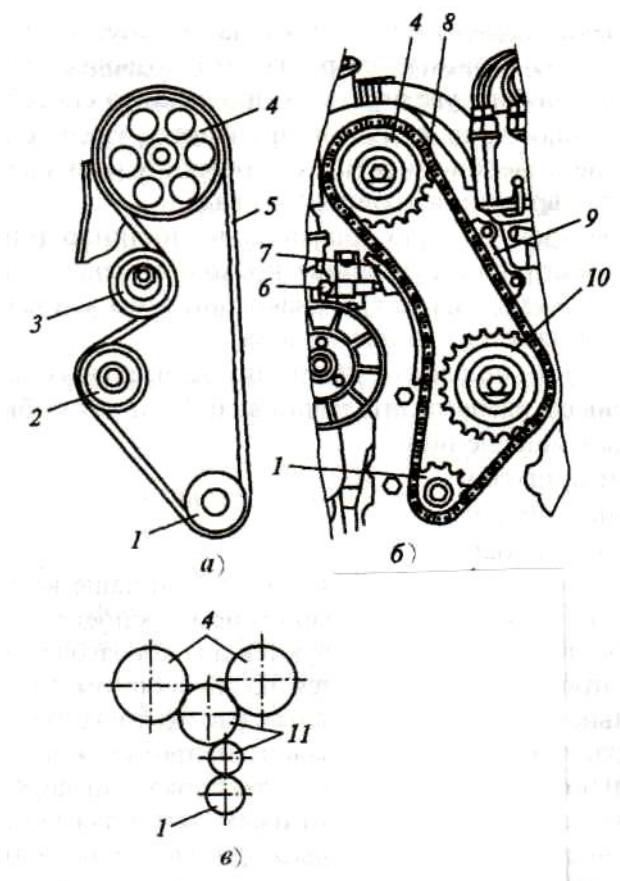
Различные способы привода распределительного вала: а — ремённый; б — цепной; в — с зубчатым зацеплением: 1 — коленчатый вал; 2 — жидкостной насос; 3 — натяжной ролик; 4 — распределительный вал; 5 — приводной ремень; 6 — натяжитель цепи; 7 — башмак натяжителя цепи; 8 — цепь; 9 — успокоитель цепи; 10 — масляный насос; 11 — промежуточный вал
